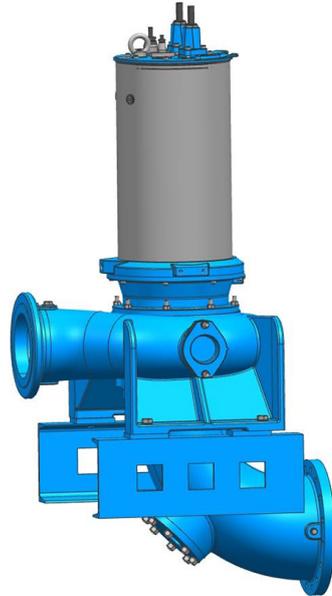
Trockenaufstellung Vertikal; ab Einpass 410 auf Betonsockel; stationär
